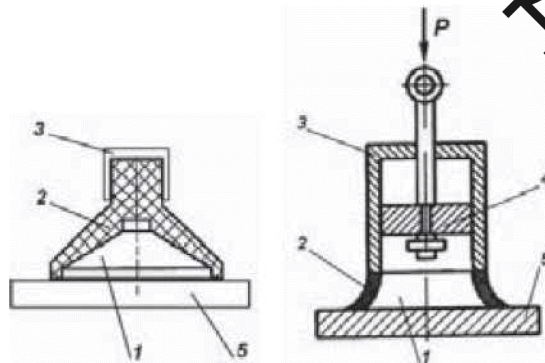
Пасивні вакуумні присмоктувачі з корпусом з еластичного матеріалу
